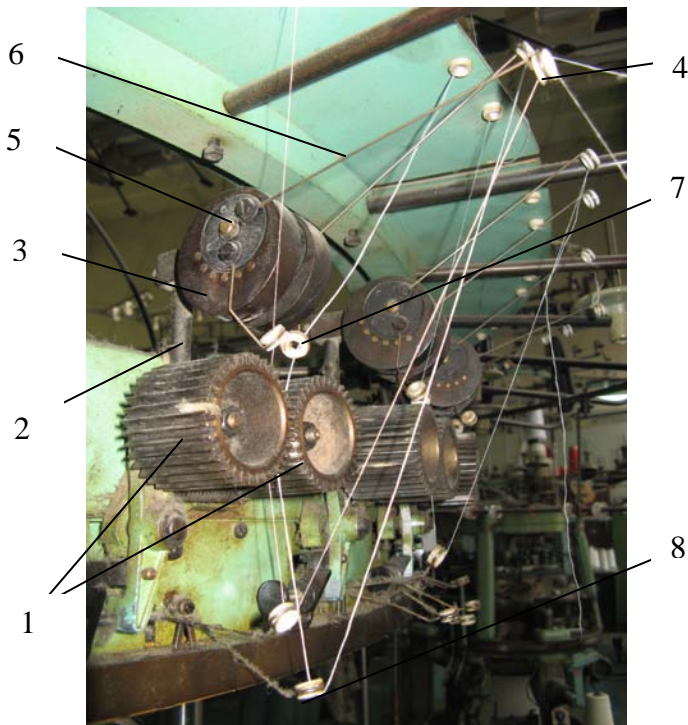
Нитеподатчик с коническими зубчатыми колесами:
